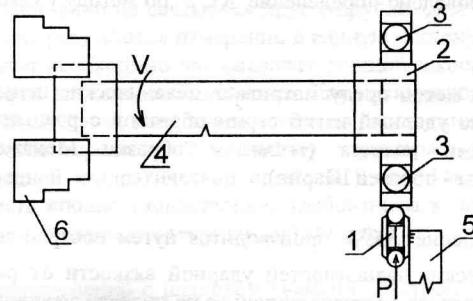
Приспособление для выращивания усталостных трещин на ударных образцах:
